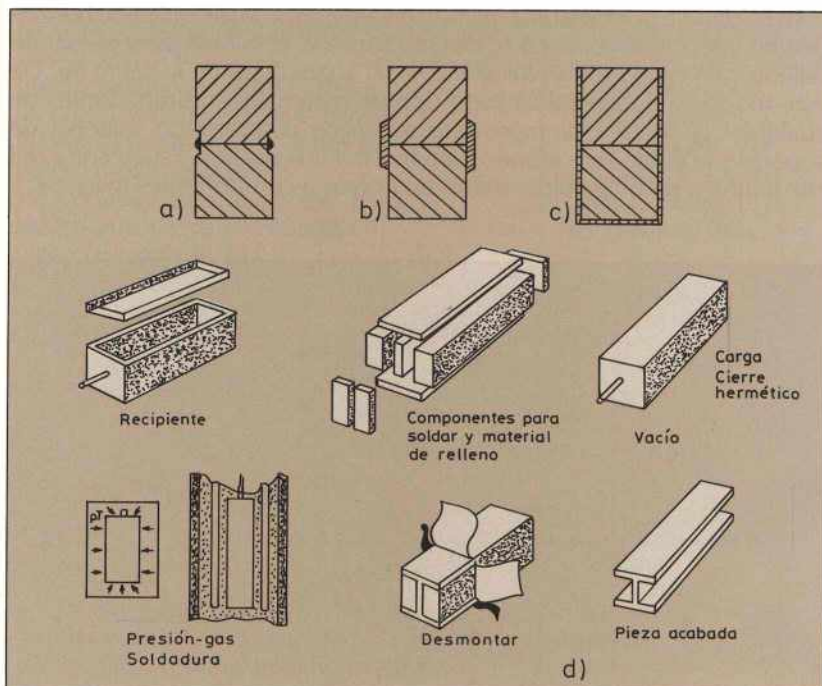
Procedimientos de soldadura por compresión isostática en caliente: a) unión a lo largo de la circunferencia de contacto; b) unión en forma de manguito alrededor de la zona de contacto; c) encapsulación hermética de los componentes a soldar; d) esquema del procedimiento c).
